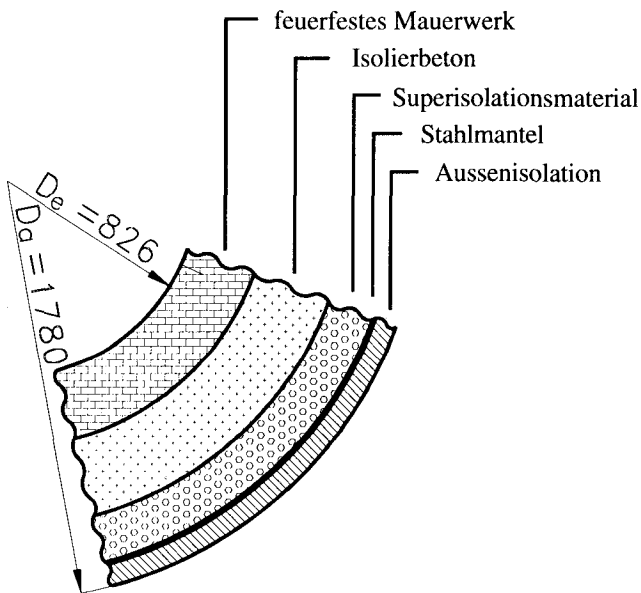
Wandaufbau des Feuerungsteils (Abmessungen in mm)
